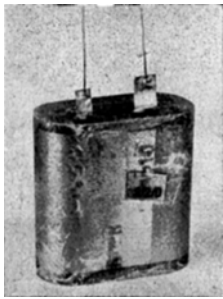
Schweißungen von Kupferdraht an Kupferfolie. (AEG)
